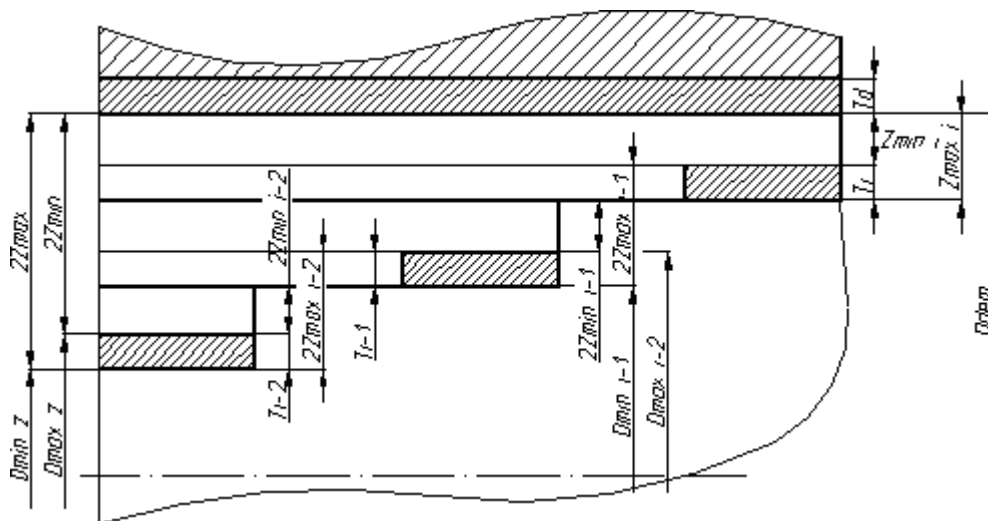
Схема связей между межпереходными размерами, припусками и допусками для охватывающих поверхностей
